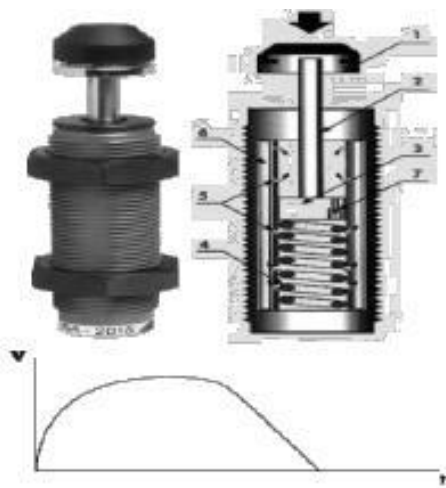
Гідравлічний амортизатор де- 1- нейлоновий упор; 2- шток поршня; 3 – поршень; 4 – зворотня пружина; 5 – отвір; 6– акумулятор; 7 – зворотній клапан.
